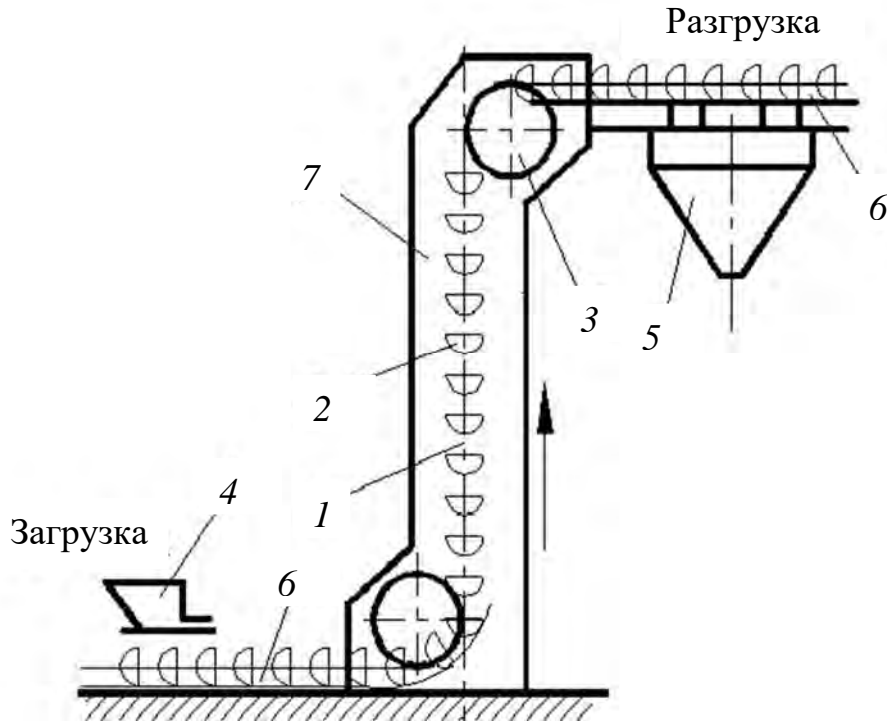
Схема скребково-ковшового конвейера: 1 – тяговая цепь; 2 – ковш; 3 – привод; 4 – питатель; 5 – приемный бункер; 6 – желоб; 7 – кожух
